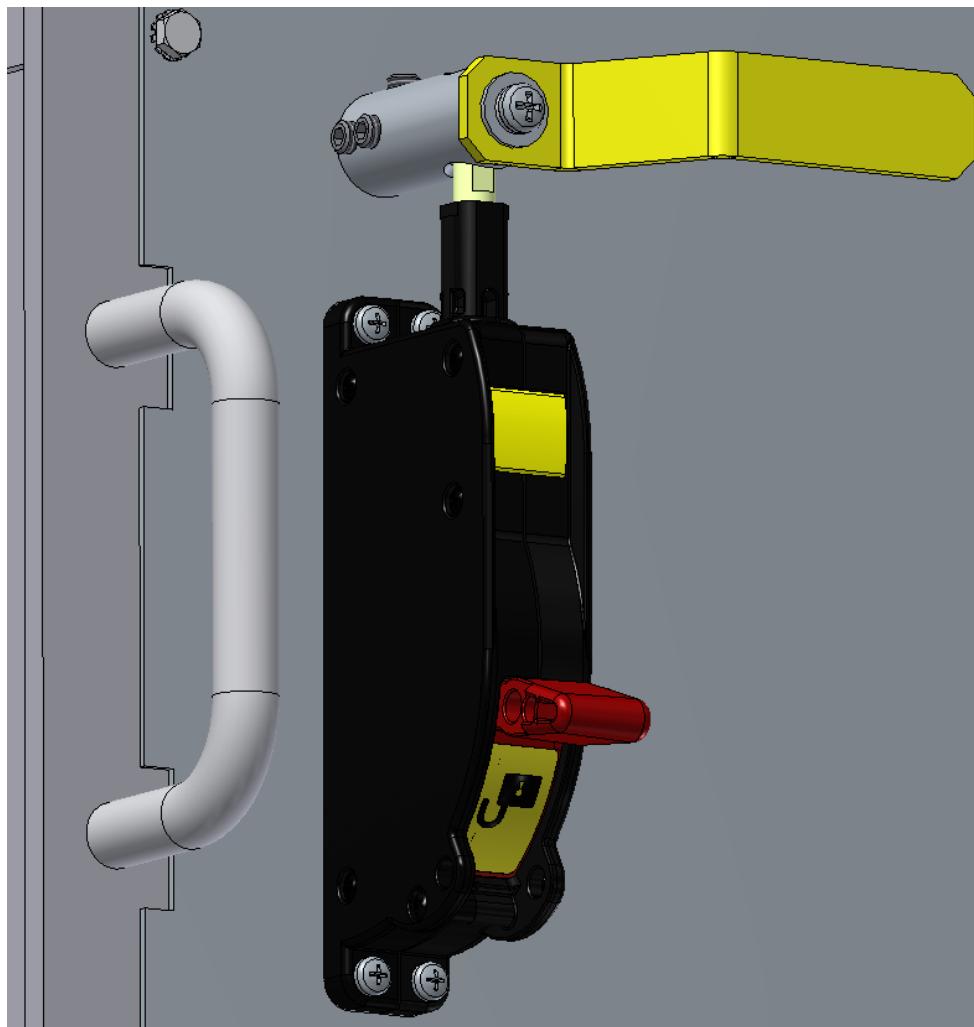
Установка блокиратора и рукоятки на фасад ВЭ
